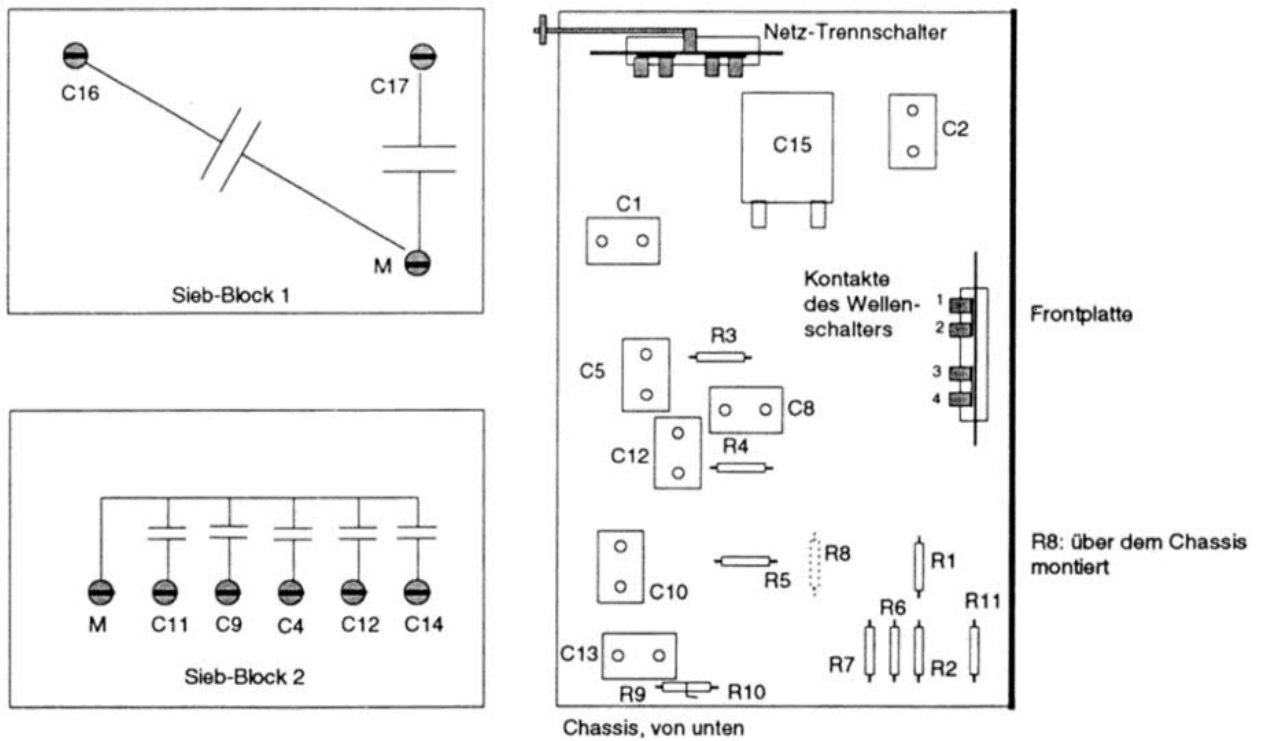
Lageplan der Bauteile unter dem Chassis des OWIN E 23 W
